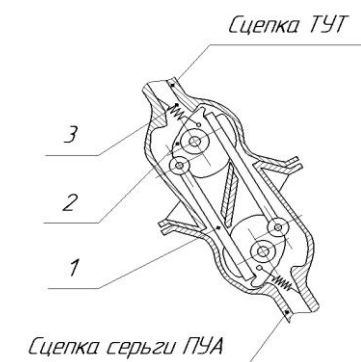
Автостык ТУТ с ПУА: 1 – серьга сцепного механизма; 2 – диск сцепного механизма; 3 – возвратная пружина
